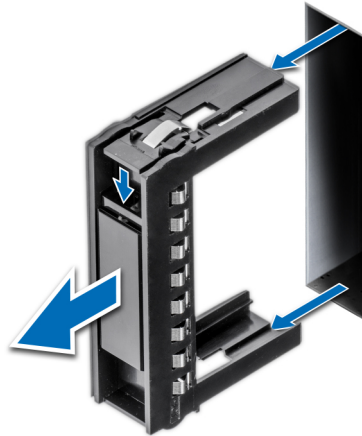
Entfernen eines Laufwerkplatzhalters
